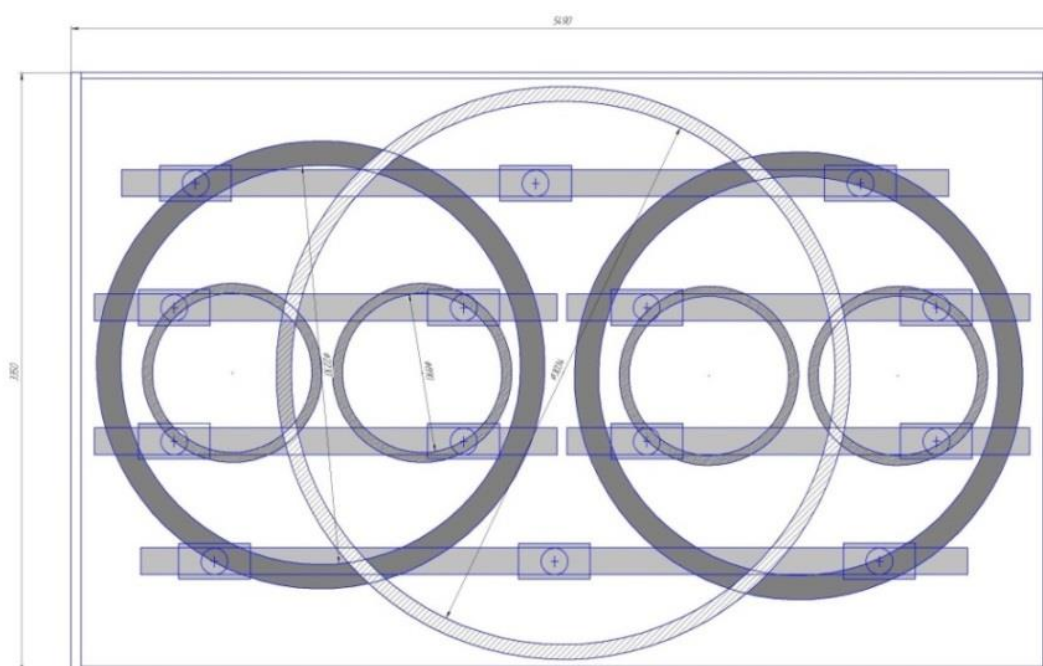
Печная телега (вид сверху) с возможным расположением на ней бандажей или колец
